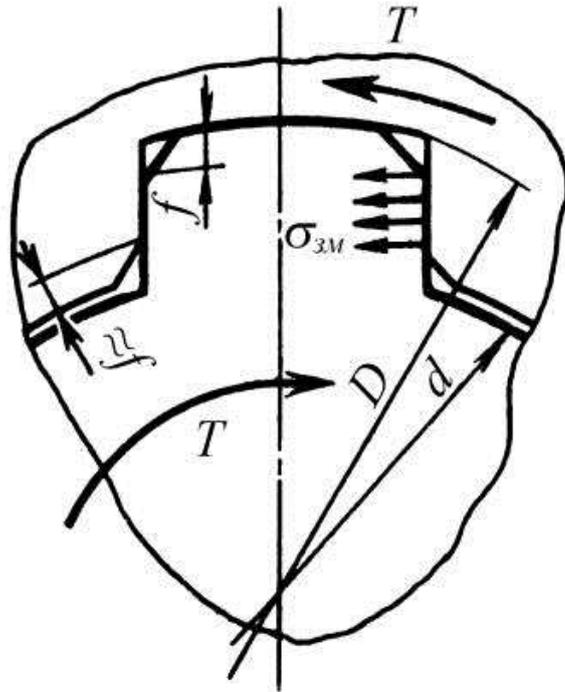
Розрахункова схема прямобічного шліцьового з'єднання
